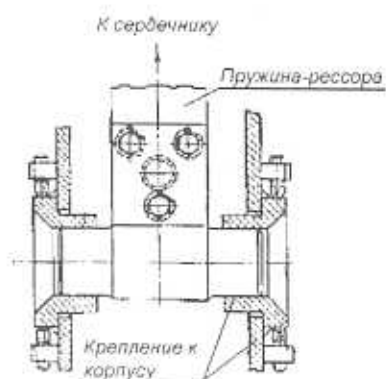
Плоская пружина для связи между сердечником и корпусом статора
